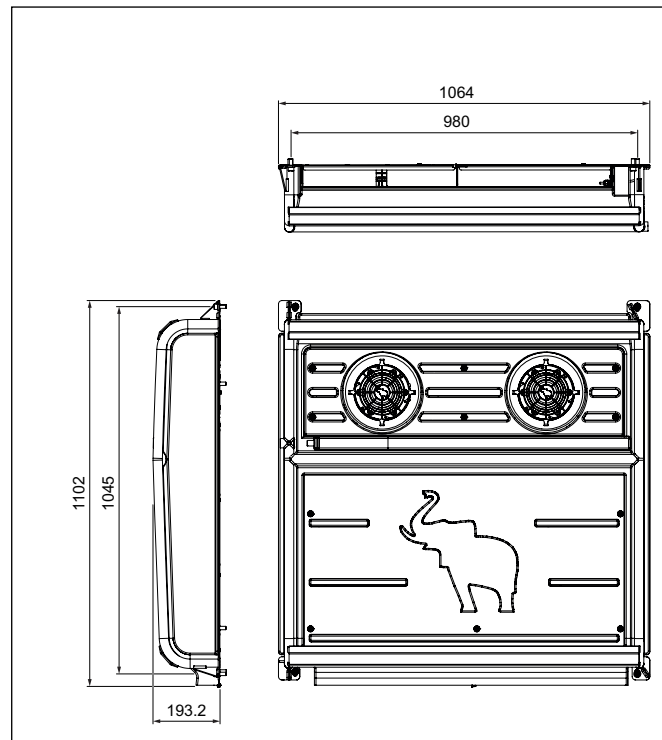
Dimensiones exteriores del evaporador adicional de techo
